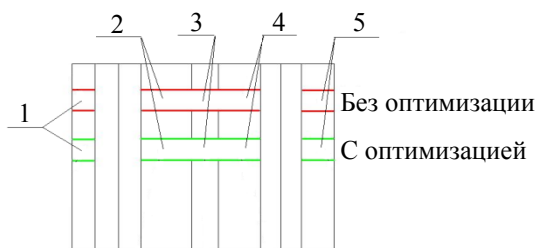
Участки заготовки для измерения шероховатости поверхности
